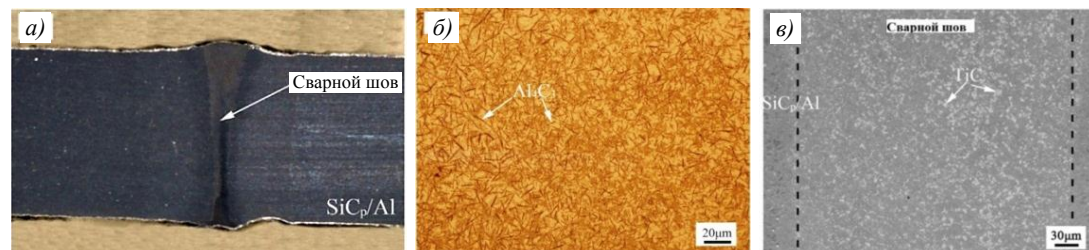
Микрофотографии сварного шва, сваренного ультразвуковой лазерной сваркой с прослойкой из титана: а – поперечное сечение соединения; б – микроструктура сварного шва; в – микроструктура, полученная на СЭМ [22]
